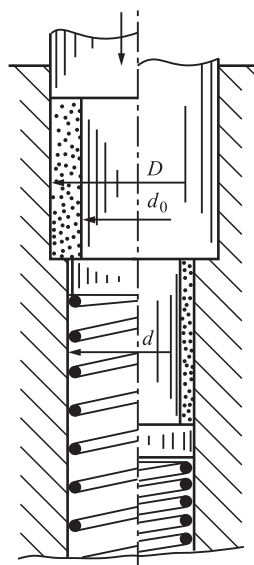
Схема нанесения обмазки на поверхность заготовки
